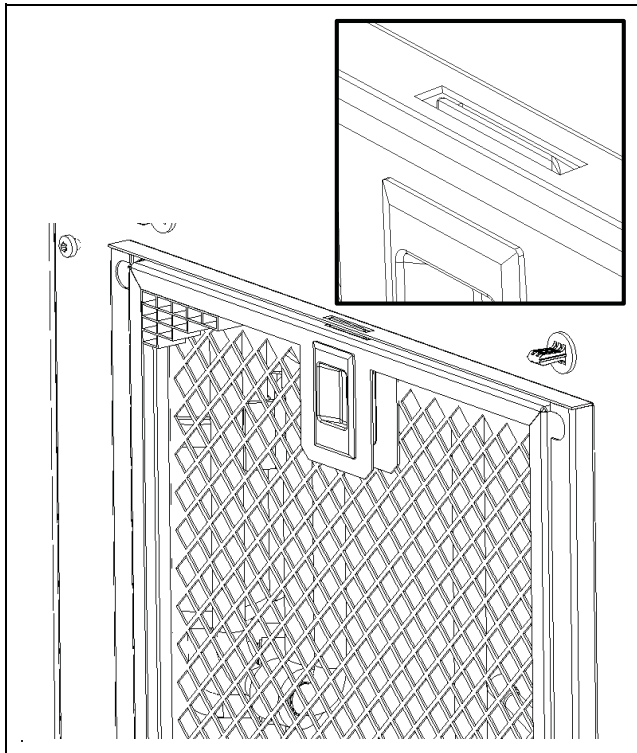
Установка металлического фильтра 3320200 и 3334300
